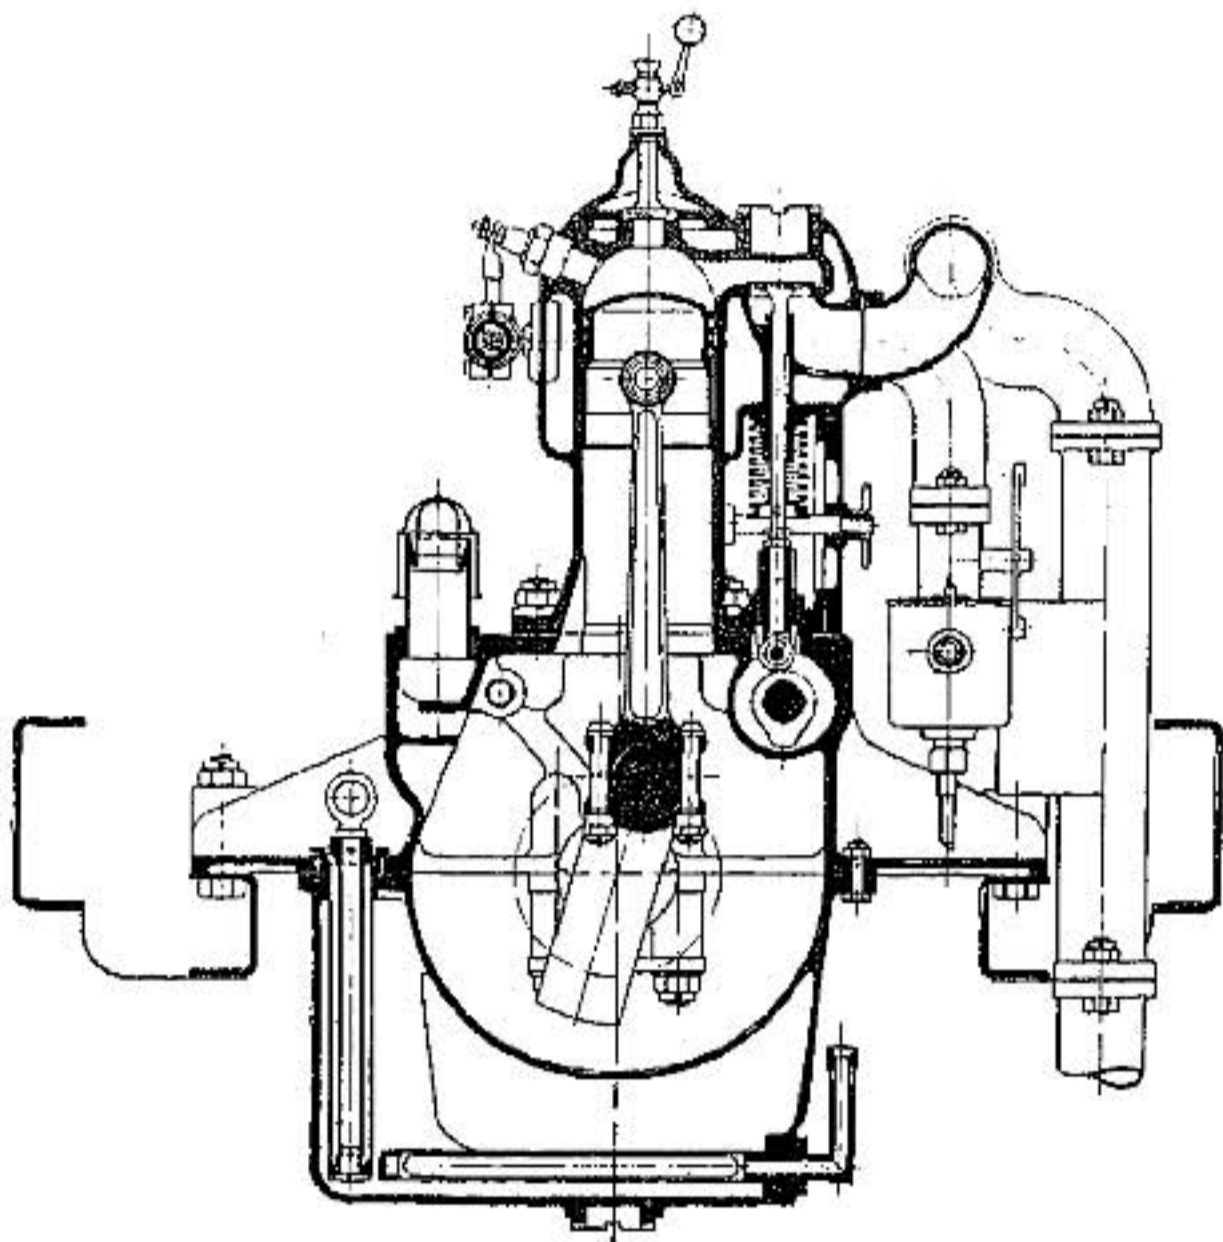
Поперечный разрѣзъ двигателя Дессау.
